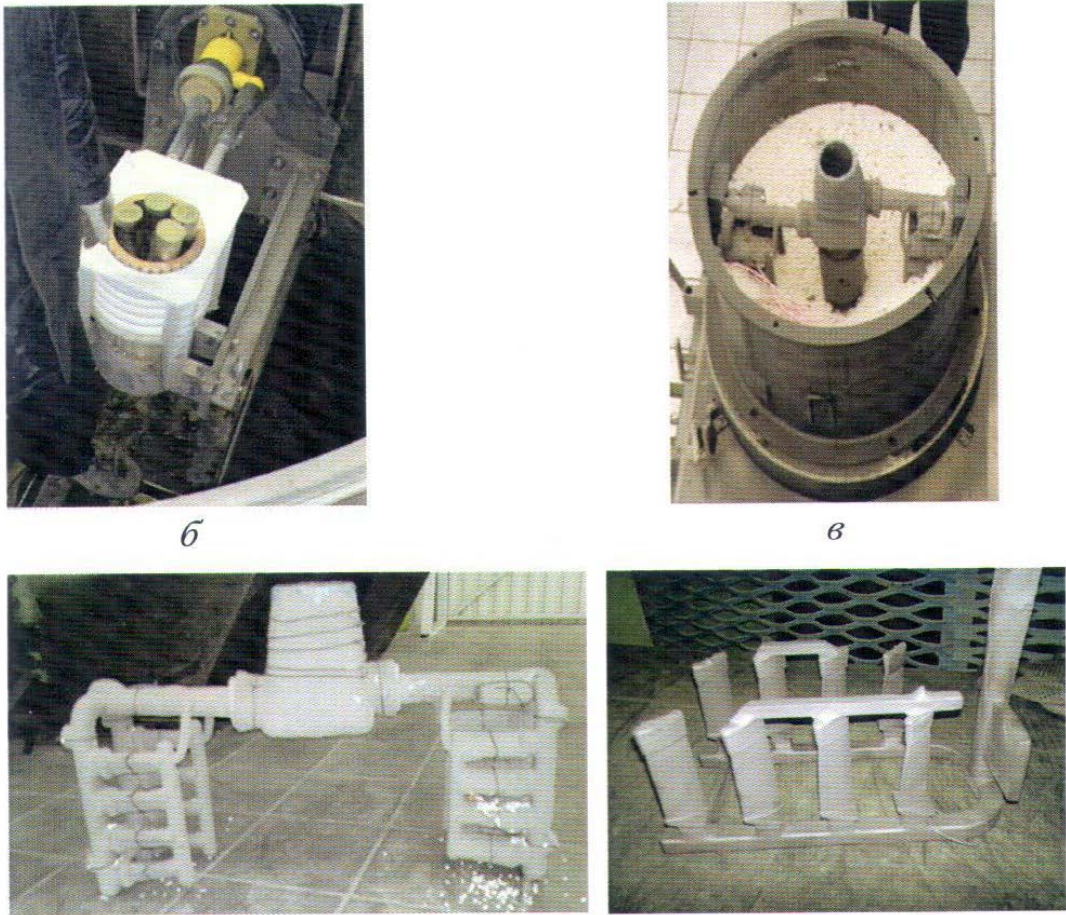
Изготовление отливок лопаток КВД [85]
